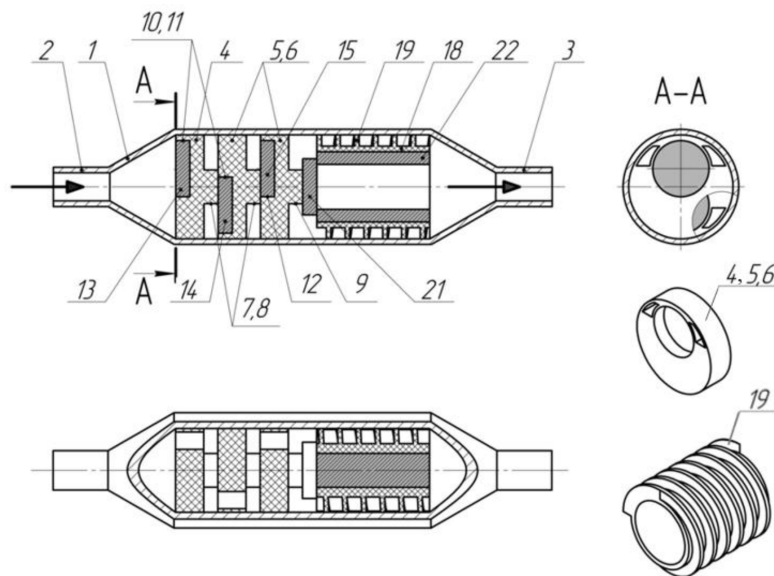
Конструктивна схема пристрою для магнітної обробки палива:
